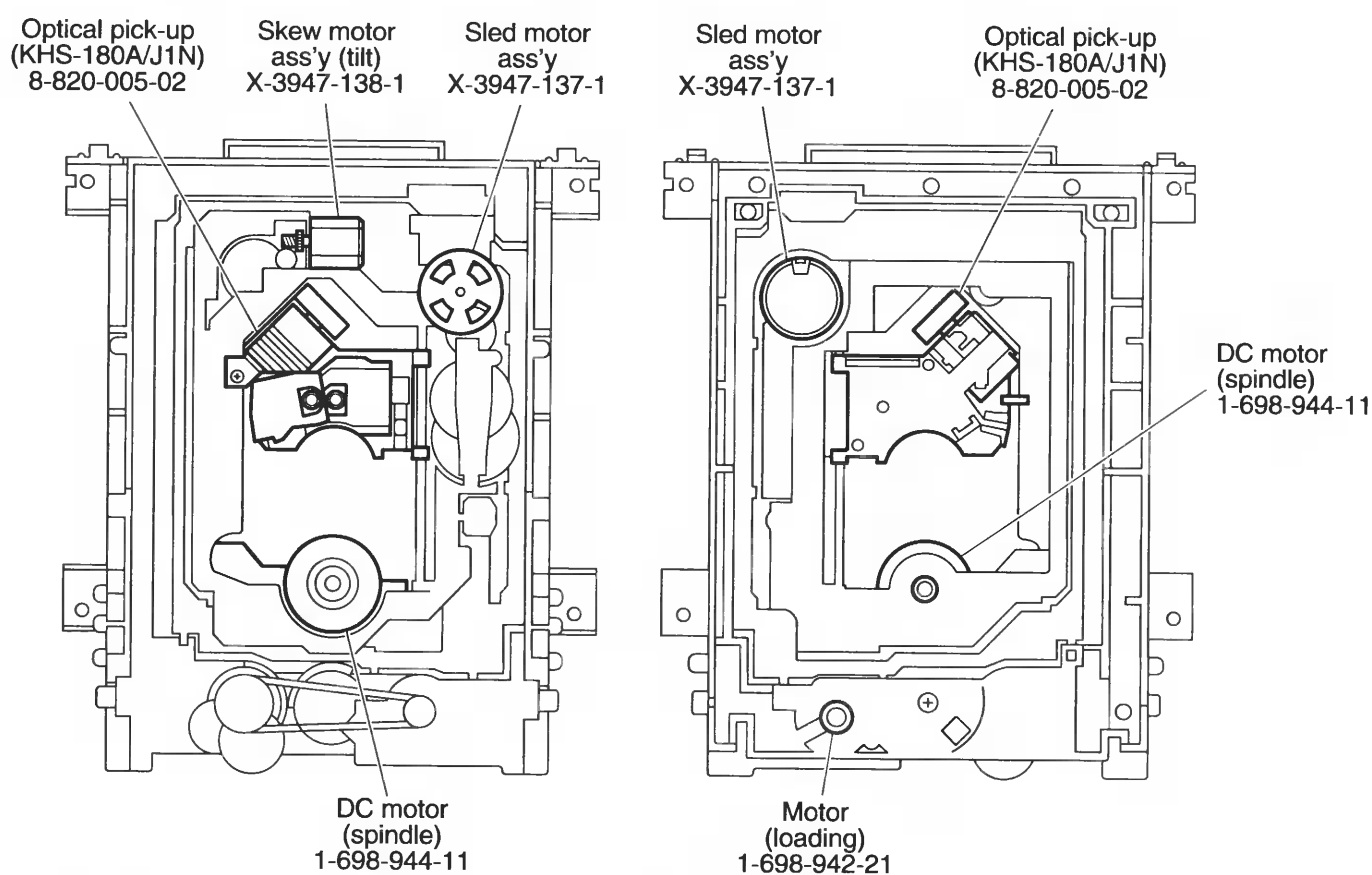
Вид сверху и снизу на устройство загрузки дисков в сборе с механизмом привода дисков
